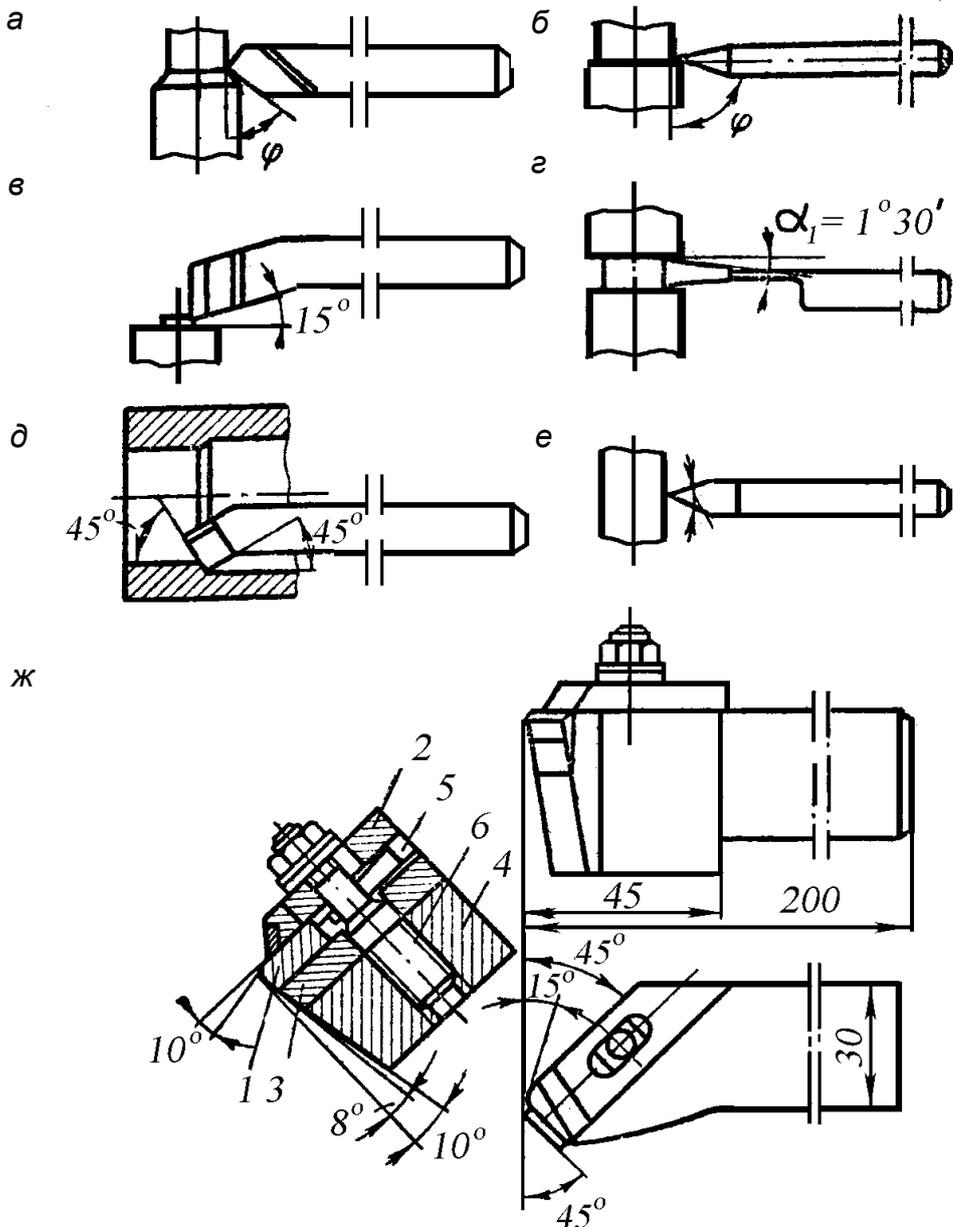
Токарные резцы: а – проходной обдирочный прямой; б – проходной чистовой с закруглением при вершине; в – подрезной; г – отрезной; д – расточный; е – резьбовой для наружной резьбы; ж – конструкции ЦНИИТМАШ с механическим креплением
